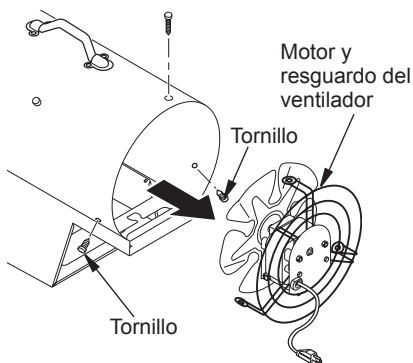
Desmontaje del motor y el resguardo del ventilador del calentador
